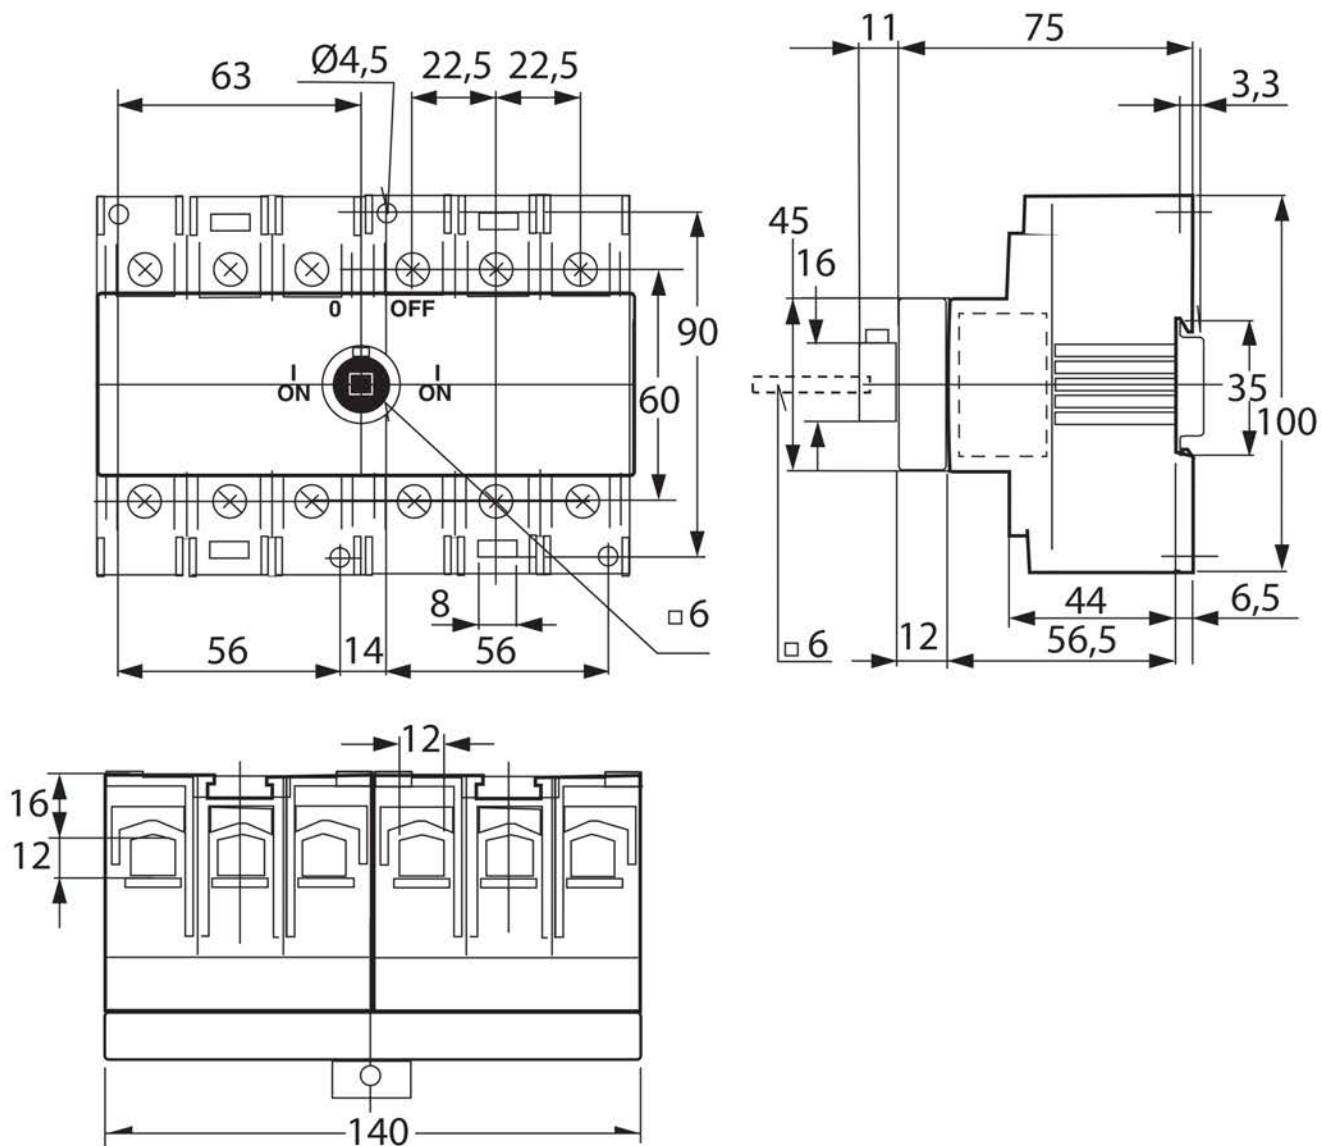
Габаритные и установочные размеры реверсивных рубильников 40-125А
